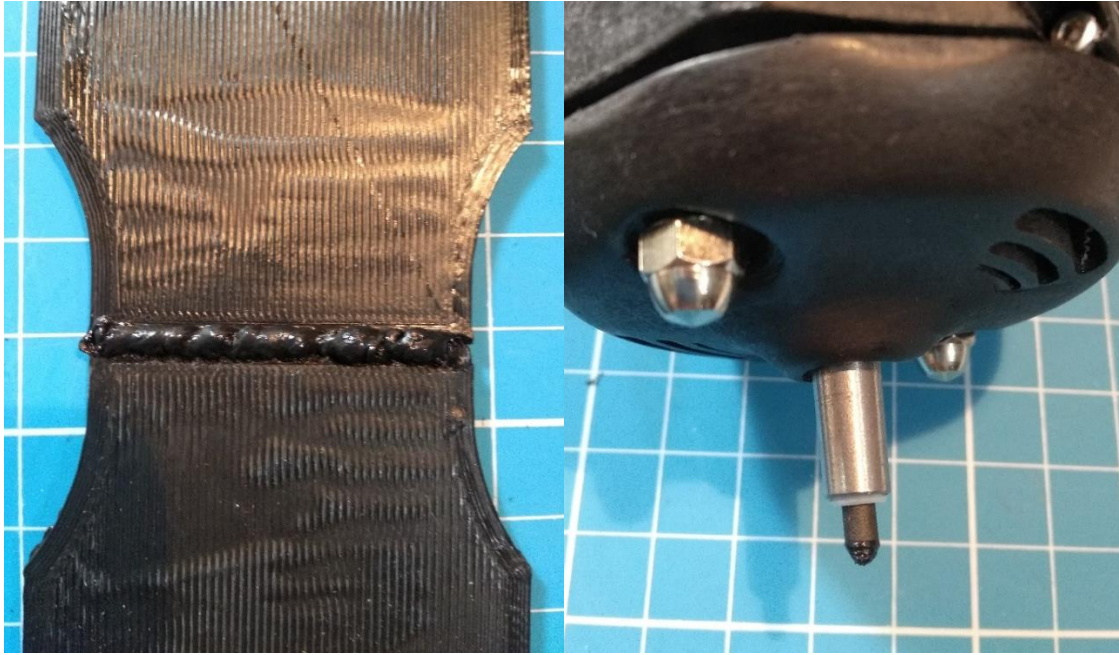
Cordón de soldadura obtenido a $2000 \text{ rpm} \pm 200 \text{ rpm}$ y 30 mm/min .
